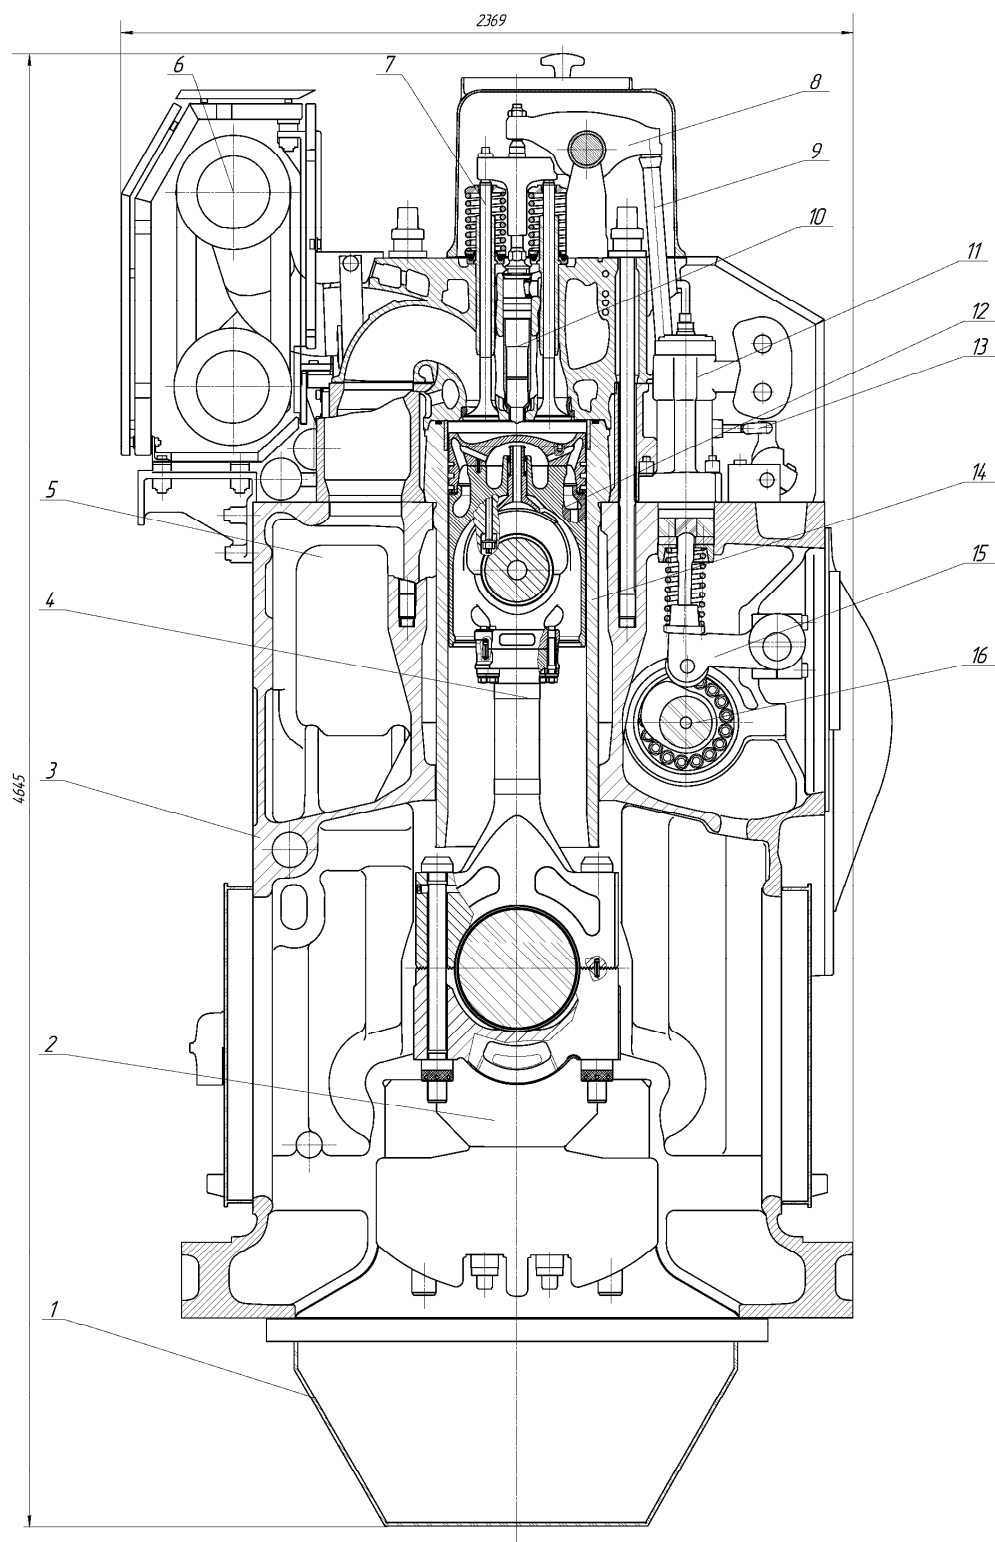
Загальне креслення головного двигуна МаК 9М32С у поперечному перетині: 1 – піддон картеру; 2 – колінчатий вал; 3 – блок-картер; 4 – шатун; 5 – повітряний ресивер; 6 – вихлопний колектор; 7 – клапани; 8 – коромисло; 9 – штанга; 10 – форсунка; 11 – паливний насос високого тиску; 12 – поршень; 13 – паливна рейка; 14 – втулка циліндра; 15 – механізм зміни кута випередження; 16 – розподільчий вал
